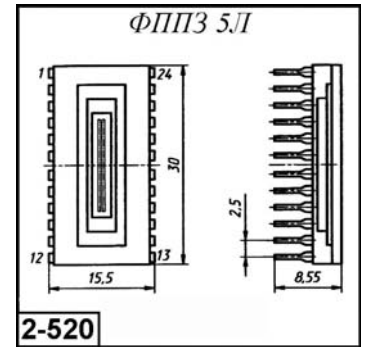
Внешний вид и габаритные размеры ФППЗ 5Л
